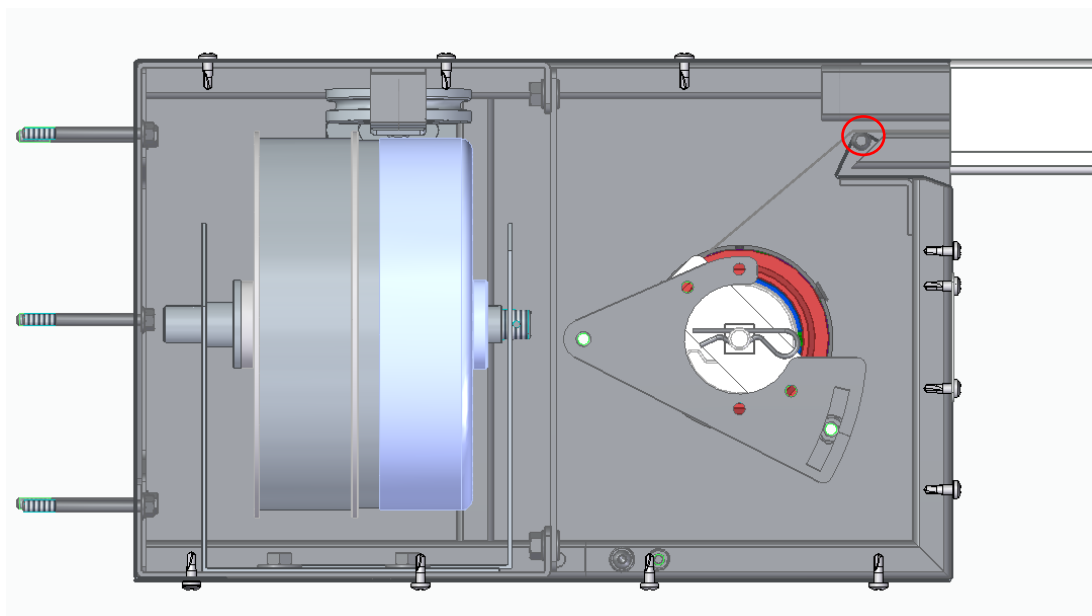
Ložiskový spoj s obráběnou maticí M6
